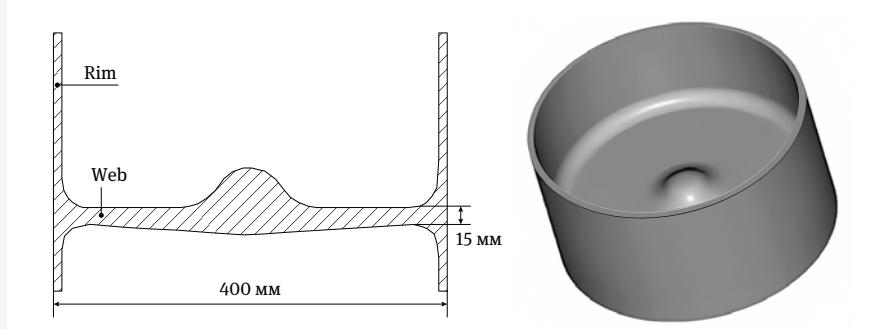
Штамповка колеса из алюминиевого сплава AA6061 [13]
